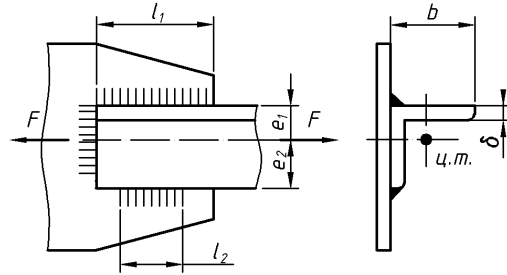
Сварное соединение полосы с косынкой
